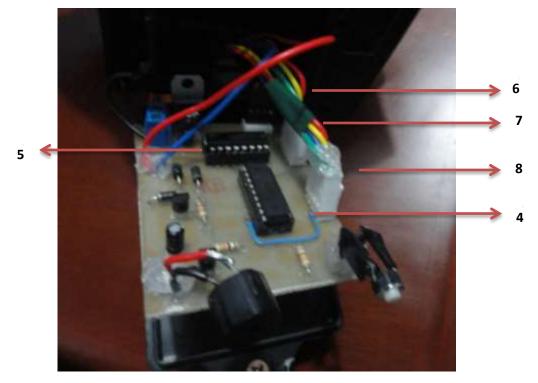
Partes que integran el módulo principal. Fuente [El Autor].
